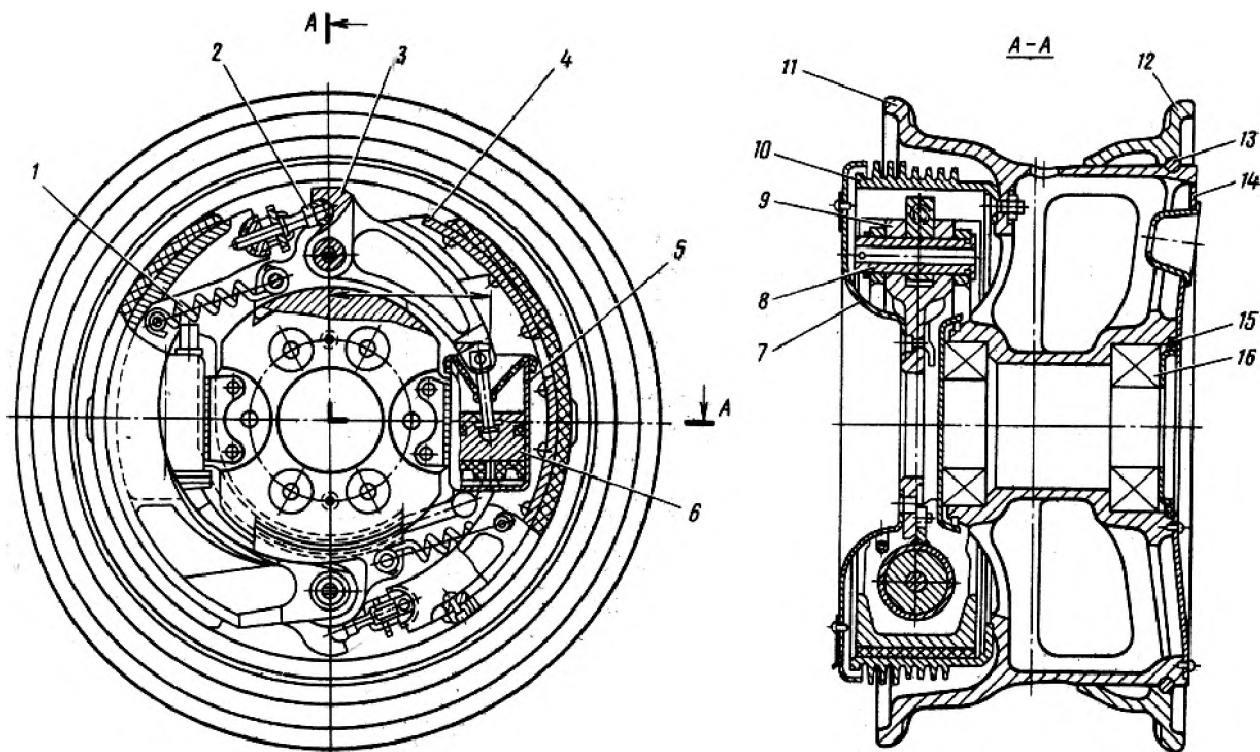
Устройство колеса главной стойки шасси вертолета Ка-26 [3]:
